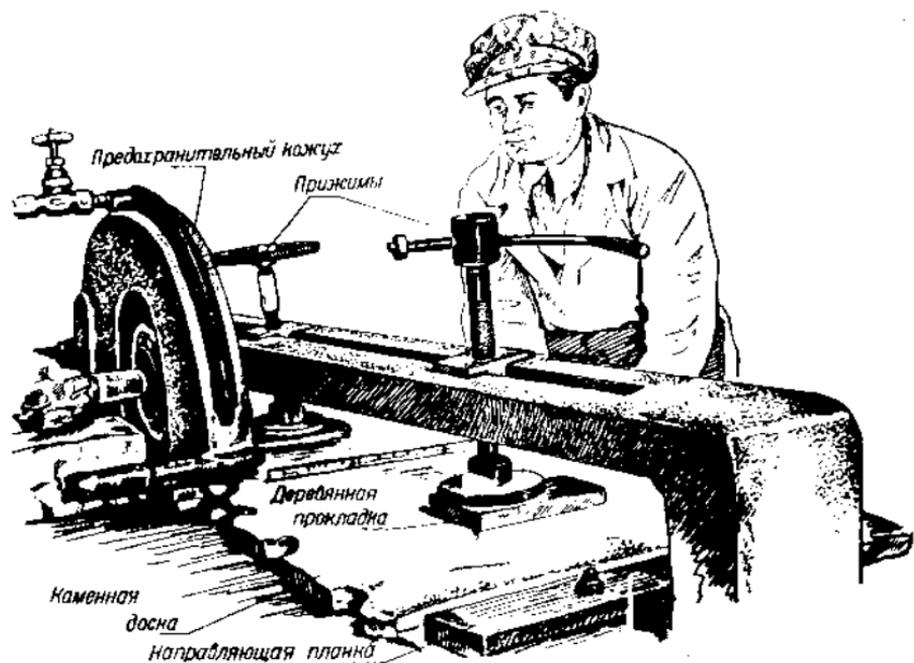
Проверка установки укрепленной каменной доски на тележке фрезерного станка с ручной подачей
